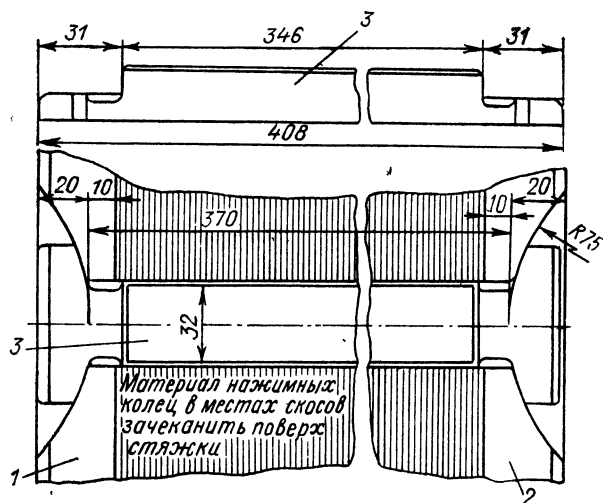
Сердечник статора тягового двигателя, стянутый стяжками
